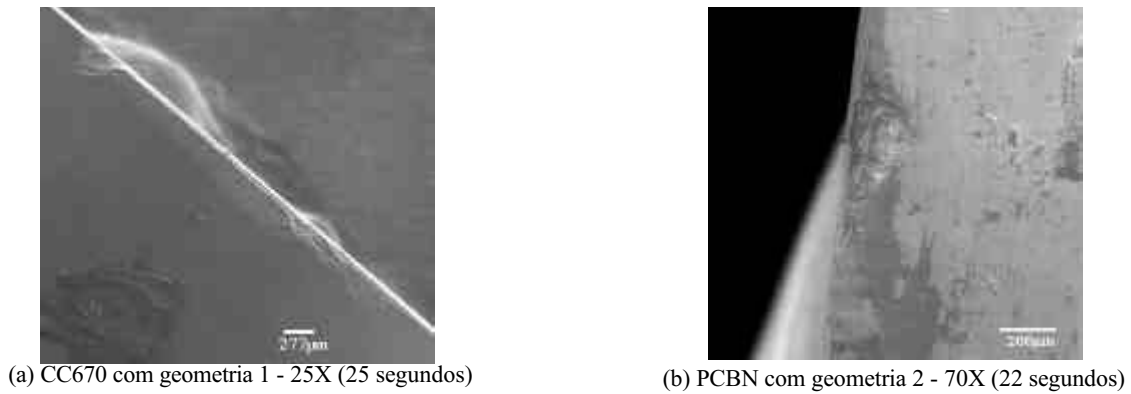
Condição de desgaste das ferramentas CC670 e PCBN.
